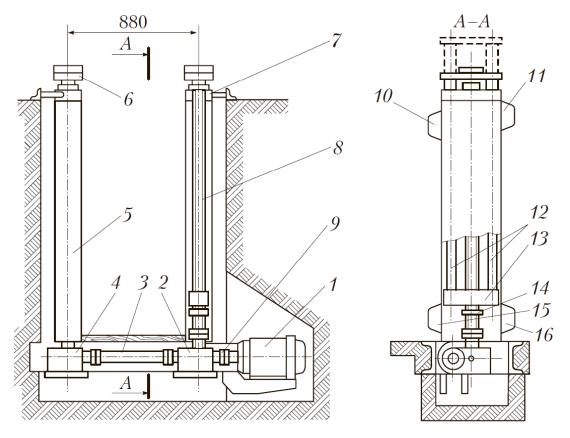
Схема двухстоечного канавного электромеханического подъемника: 1 — электродвигатель; 2 и 4 — червячные редукторы; 3 — карданная передача; 5 — стойка; 6 — верхняя траверса; 7 — опора ходового винта; 8 — ходовой винт; 9 — муфта; 10 и 15 — концевые выключатели; 11 и 16 — контрольные выключатели; 12 — штанги; 13 — нижняя траверса с грузоподъемной гайкой; 14 — страхующая гайка
